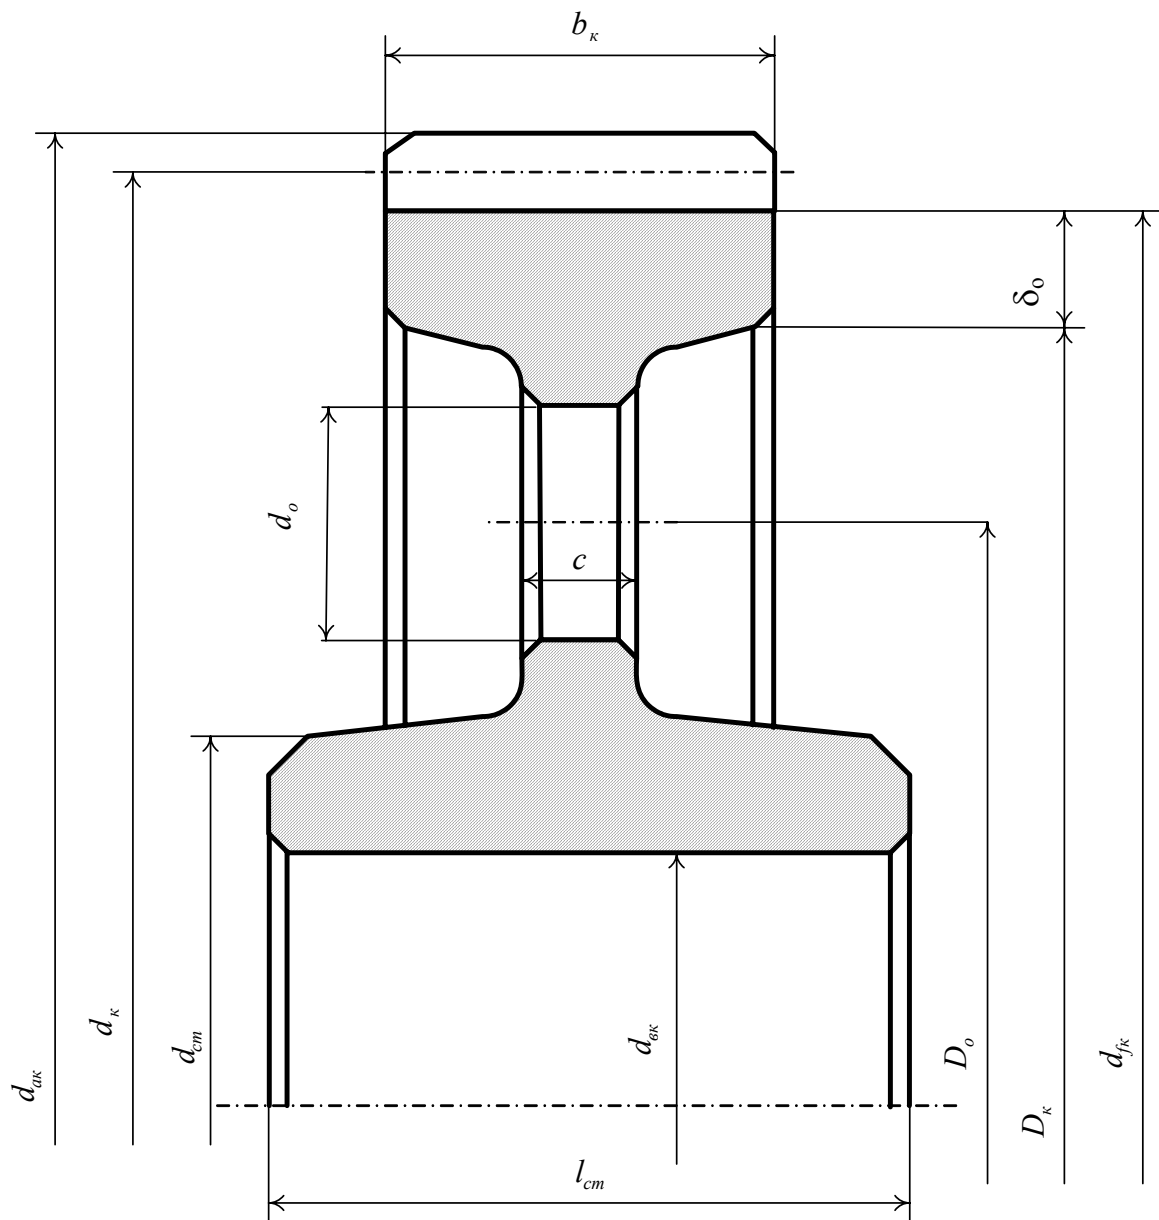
Конструкція колеса із заготовки, що отримано вільною ковкою
